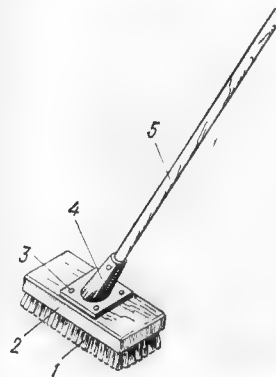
1 — пучок; 2 — корпус; 3 — шуруп; 4 — тулейка; 5 — ручка
